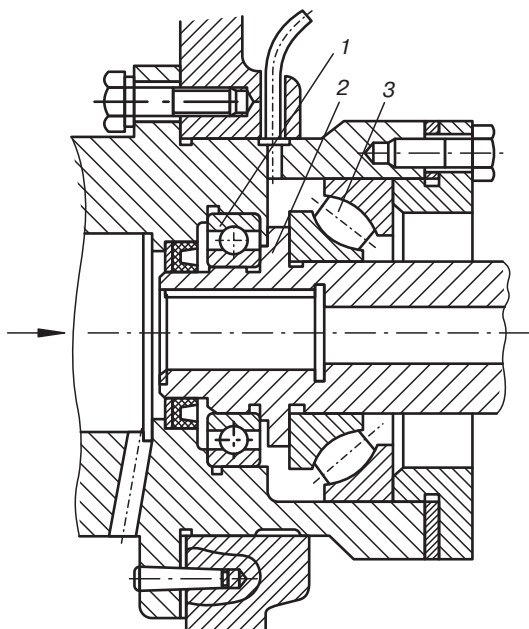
Схема узла подшипников одношнекового экструдера со сферопорным подшипником
